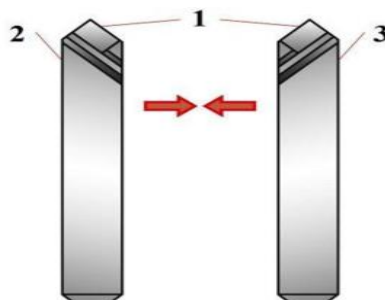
Определение резцов по направлению подачи: 1 – главная режущая кромка; 2 – левый резец; 3 – правый резец
